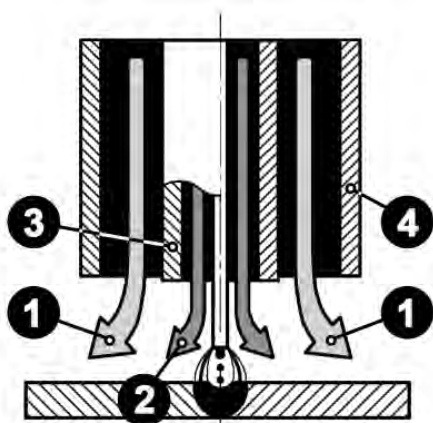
Принципиальная схема двухструйной коаксиальной подачи защитных газов в зону сварки: 1 – кольцевой поток углекислого газа; 2 – центральный струйный поток аргона; 3 – внутренний трубчатый канал сопла горелки; 4 – внешний кольцевой канал сопла горелки
